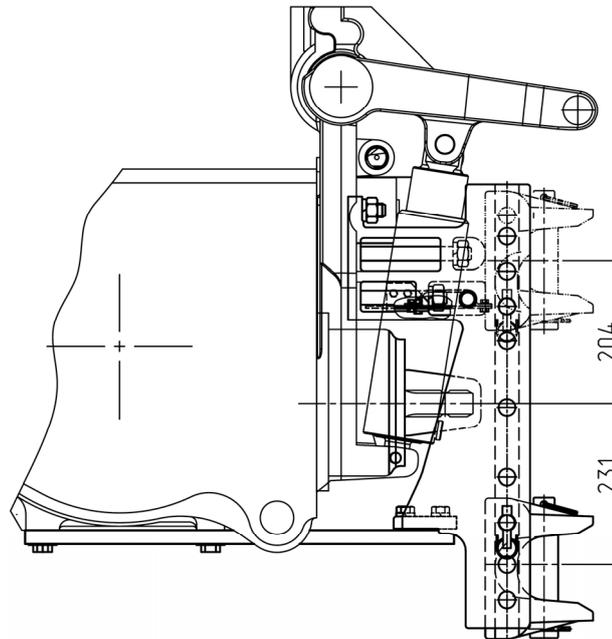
Схема вариантов установки вилки не вращающейся
